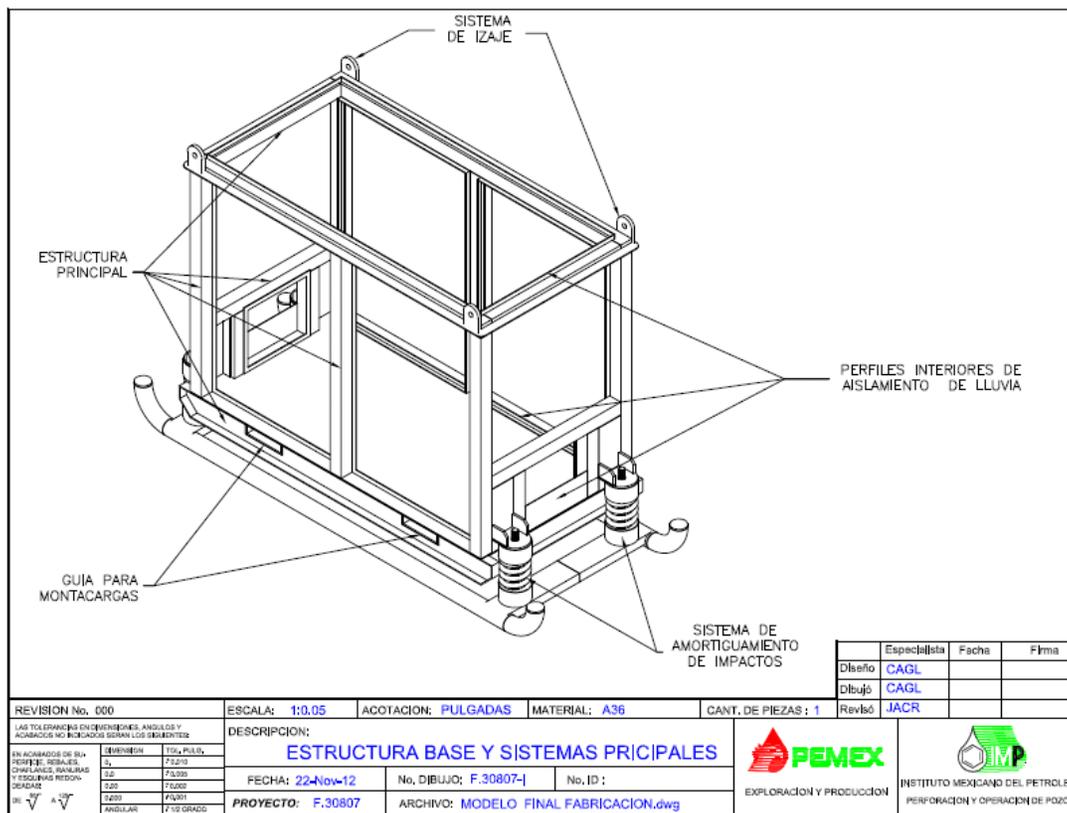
Plano de la estructura base y los sistemas principales del diseño conceptual.
